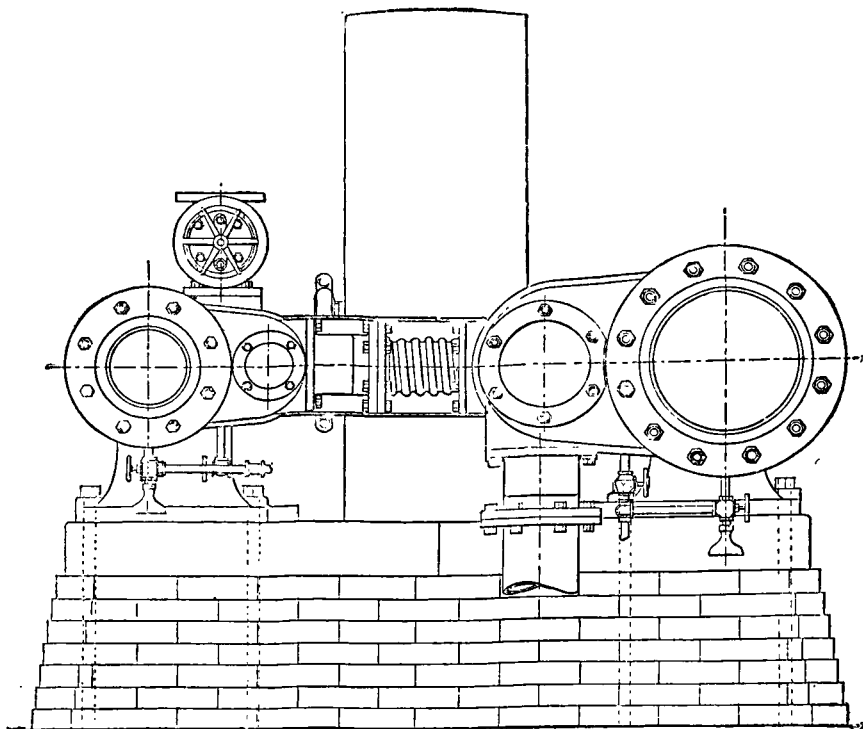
Machine compound jumelle. Vue d'arrière.
